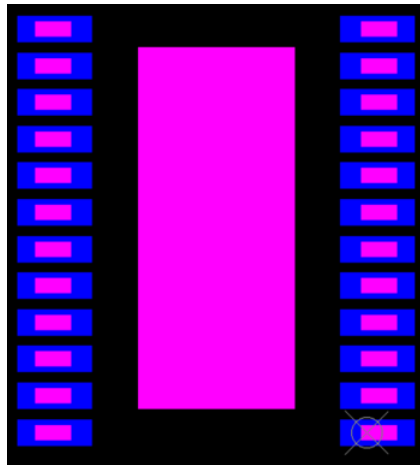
另一 SO-24 PCB 焊盘上的 PWP0024T，粉色：TI PWP0024T 引线，蓝色：其他 SO-24 PCB 焊盘
